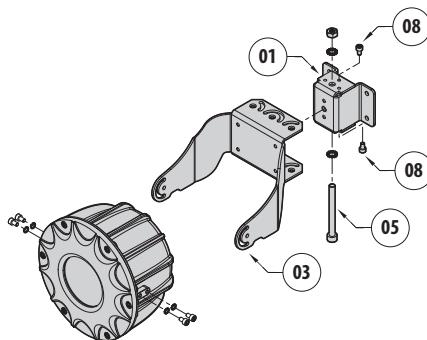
Fissaggio a parete con ingresso cavi verso il basso.
